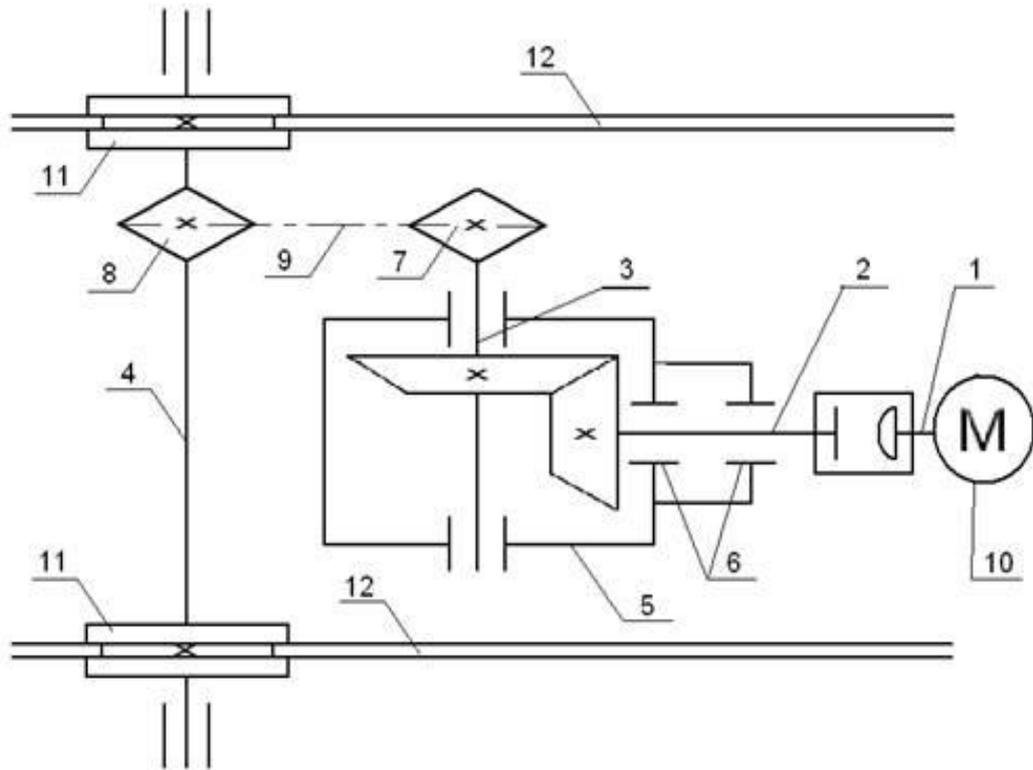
Кинематическая схема привода с коническим зубчатым редуктором
